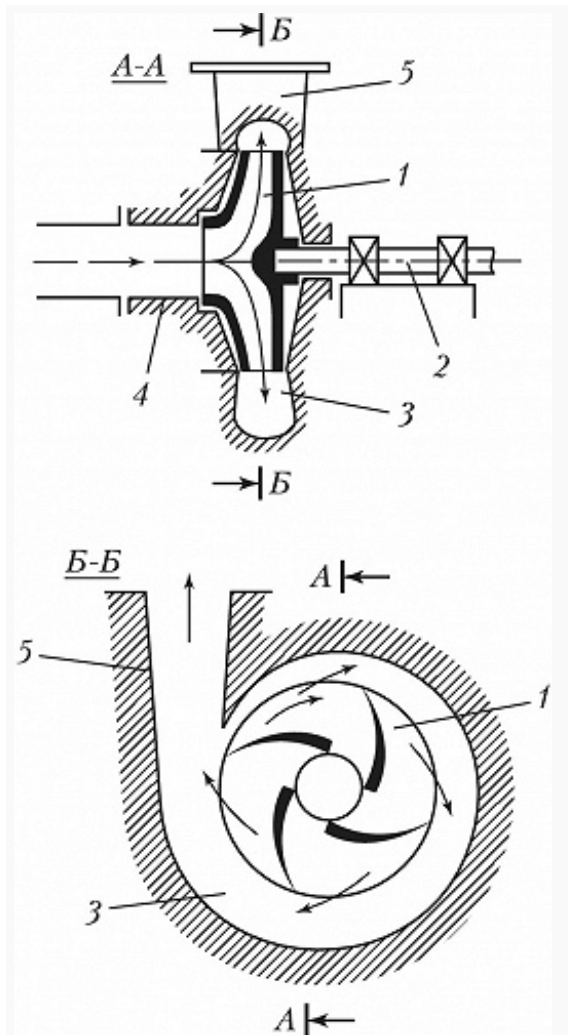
Схема центробежного насоса: 1 – лопастное рабочее колесо; 2 – приводной вал; 3 – напорная камера; 4 – всасывающий патрубок; 5 – напорный патрубок.
